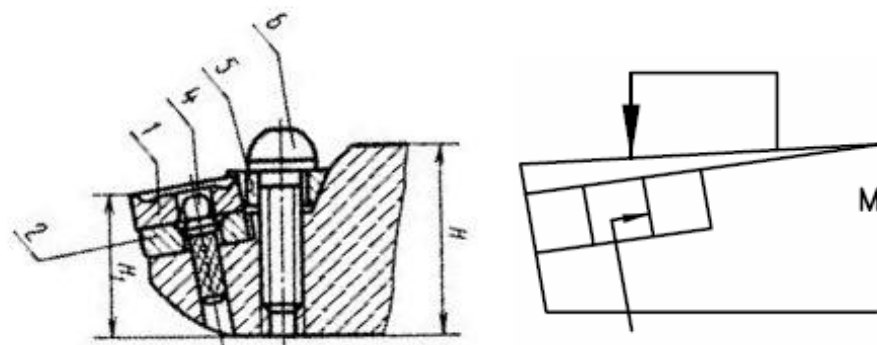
Кріплення твердосплавної змінної пластини клином-прихватом:
